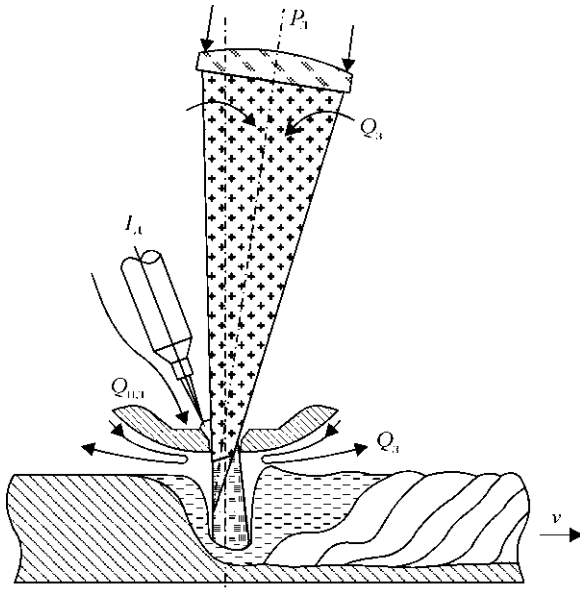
Схема процесса гибридной лазерно-плазменной сварки нержавеющей стали: $P_{\text{л}}$ — мощность лазерного излучения; v — скорость сварки; $I_{\text{д}}$ — ток дуги; $Q_{\text{пл}}$ — расход плазмообразующего газа; $Q_{\text{з}}$ — расход защитного газа
